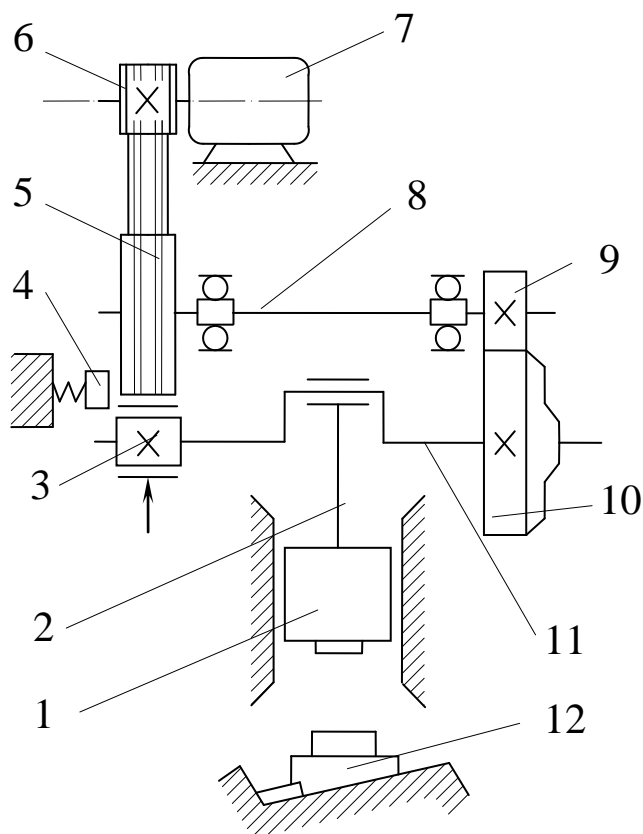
Схема гарячештампувального кривошипного преса
